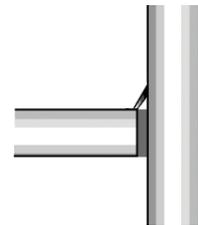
Écart de 2,5 mm (3/32 po) après soudage
